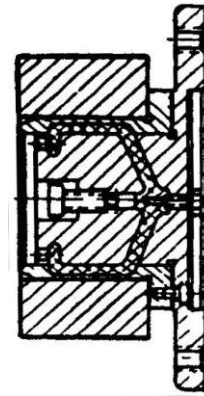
Установка заготовок на розтискній оправці з гідропластом
